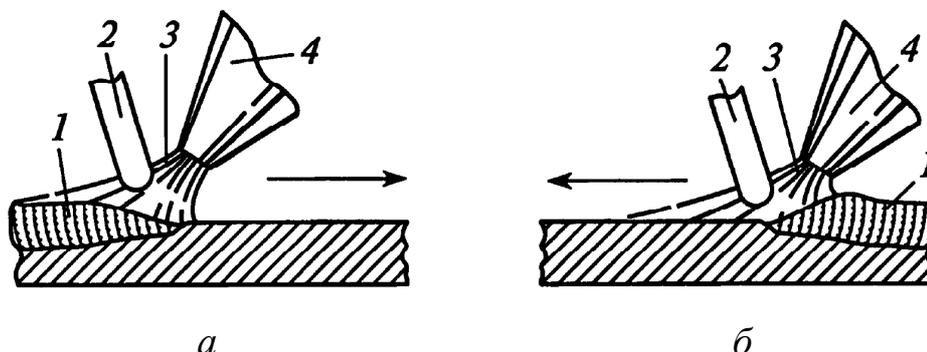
Основные способы газовой сварки: *a* – правый способ сварки; *б* – левый способ сварки; 1 – формирующий шов; 2 – присадочный пруток; 3 – пламя горелки; 4 – горелка
